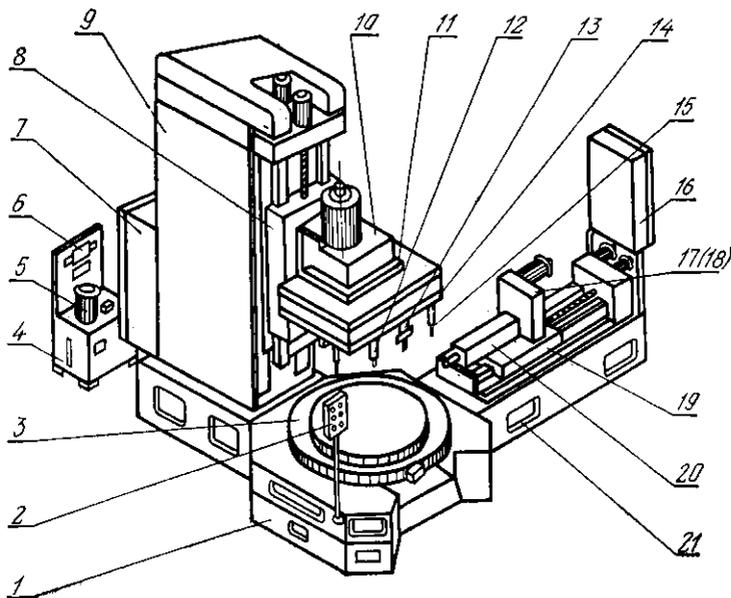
Схема компоновки агрегатного станка с поворотным столом
